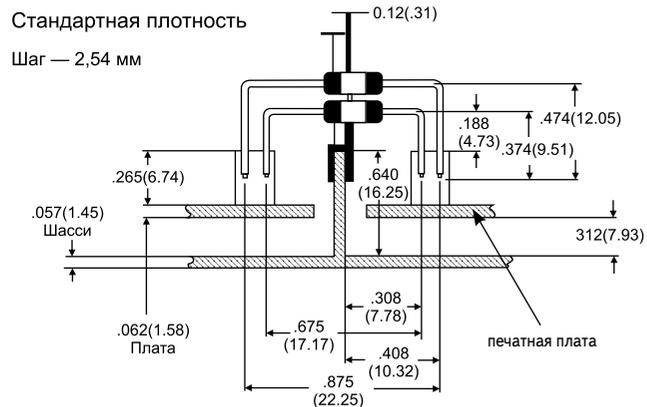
Типовой пример монтажа сборки серии Easy Mate Filter Plates
